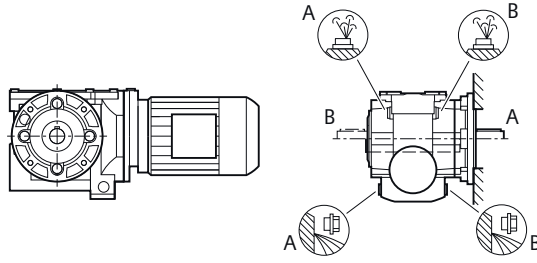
Helezon düz dişli için montaj konumları CAD Geçmeli model Yapı boyutu 39A
